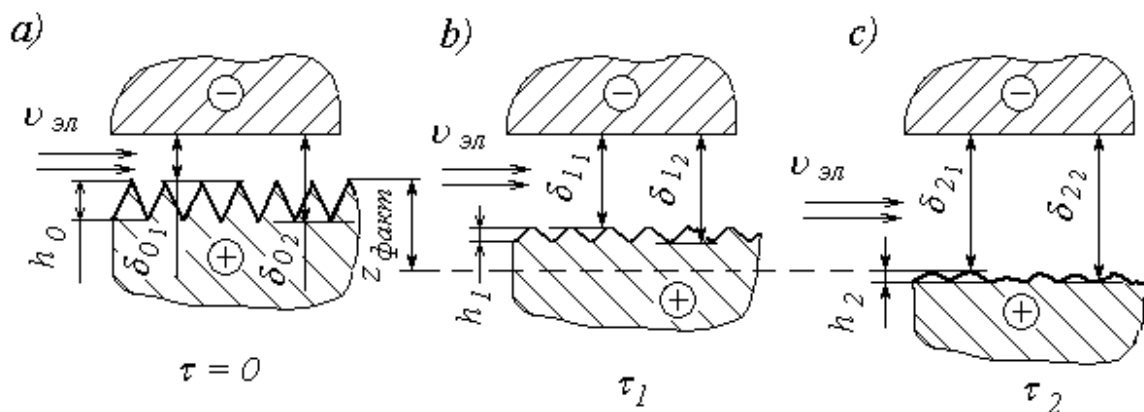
Этапы удаления исходной шероховатости с поверхности заготовки
